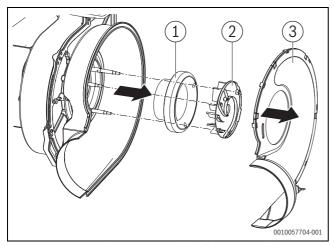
Smontaggio dei componenti del collettore di ventilazione
